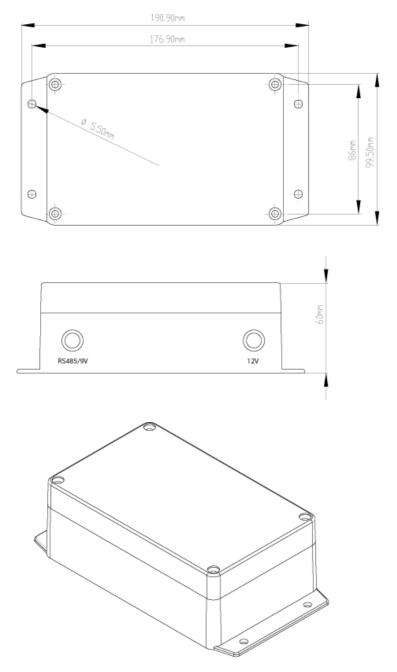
Внешний вид, габаритные и крепежные размеры блока.
